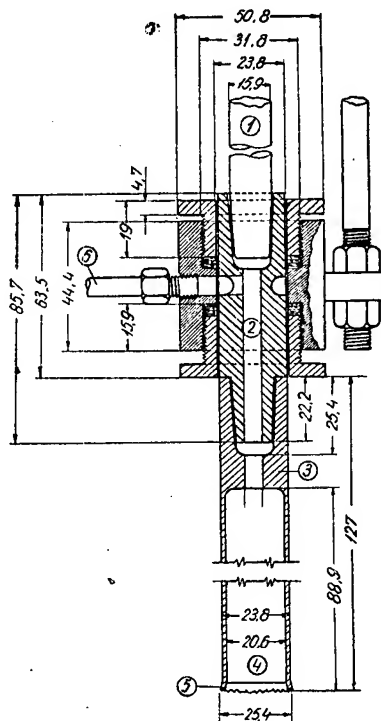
Freză specială pentru tăiat cilindri de probă din carote: 1 — axul de comandă; 2 — piesa de cuplaj (avînd rolul « capului de injecție » de la instalația de foraj); 3 — corpul frezei; 4 — locașul probei; 5 — inserții de diamante industriale (boarts); 6 — intrarea aerului.
